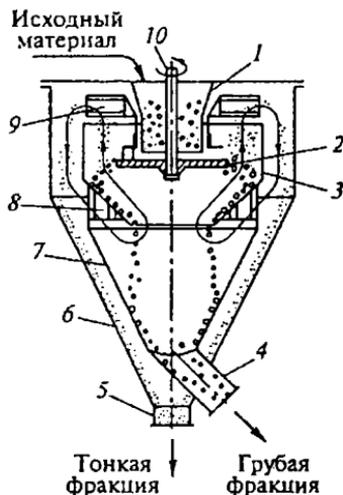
Схема воздушно-циркуляционного сепаратора: 1, 4, 5 — патрубки; 2 — диск; 3, 7 — конусы; 6 — корпус; 8 — лопатки завихрителя; 9 — вентиляторное колесо; 10 — вал
